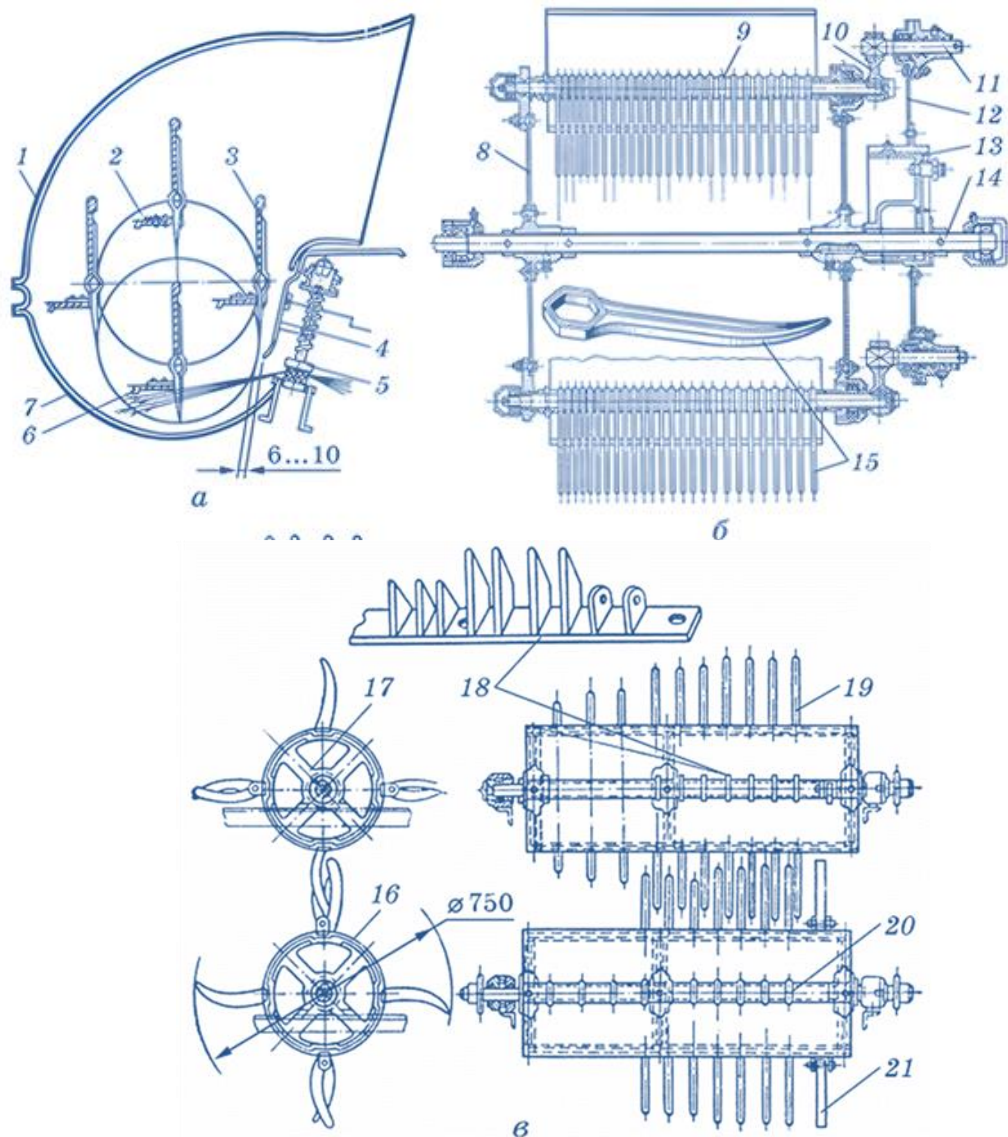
Обчісувальні апарати: а – однобарабанний; б – обчісувальний барабан; в – двобарабанний; 1 – кожух; 2 – обчісувальний барабан; 3 – вертикальна лопать; 4 – обмежувальний лист; 5 – затискний конвеєр; 6 – горизонтальна лопать; 7 – піддон; 8 – диск; 9 – гребінка; 10 – кривошип; 11 – палець; 12 – напрямний диск; 13 – ексцентрик; 14 – вал; 15 – зуб гребінки; 16 – нижній барабан; 17 – верхній барабан; 18 – короткий гребінь; 19 – довгий гребінь; 20 – вал; 21 – перетрушувач снопів.
